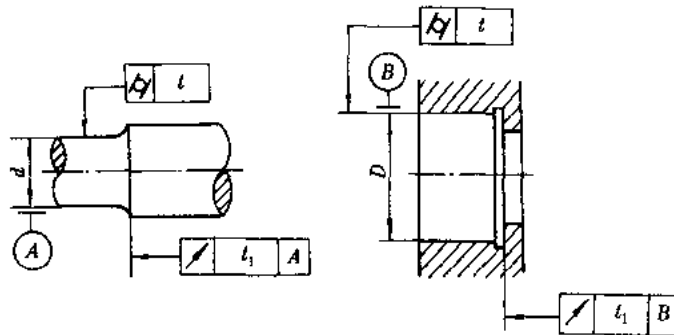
配合表面的圆柱度公差和端面圆跳动量
